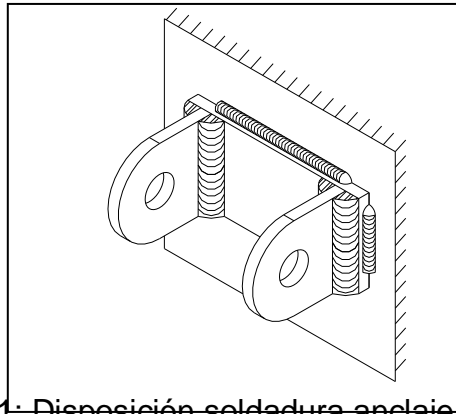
Disposición soldadura anclaje de suspensión
